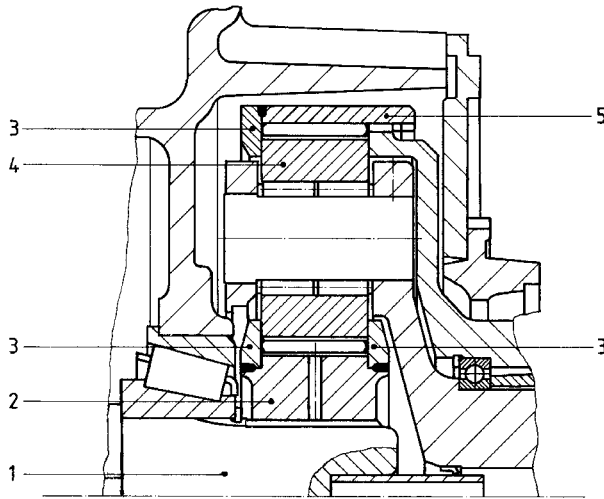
Druckkammeinsatz im Planetengetriebe mit Schrägverzahnung; 1) Hauptwelle; 2) Sonnenrad; 3) Druckkämme bzw. Axialkraftaufnahme mittels Anlaufringen; 4) Planetenrad; 5) Hohlrad /5/
